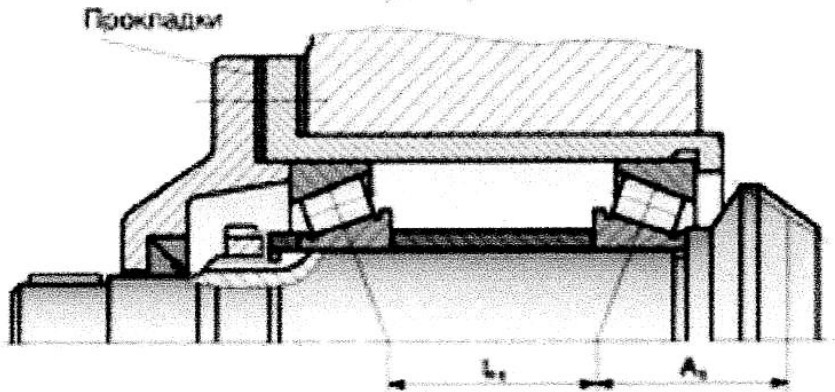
Конструкция вала с установкой подшипников «в распор».
